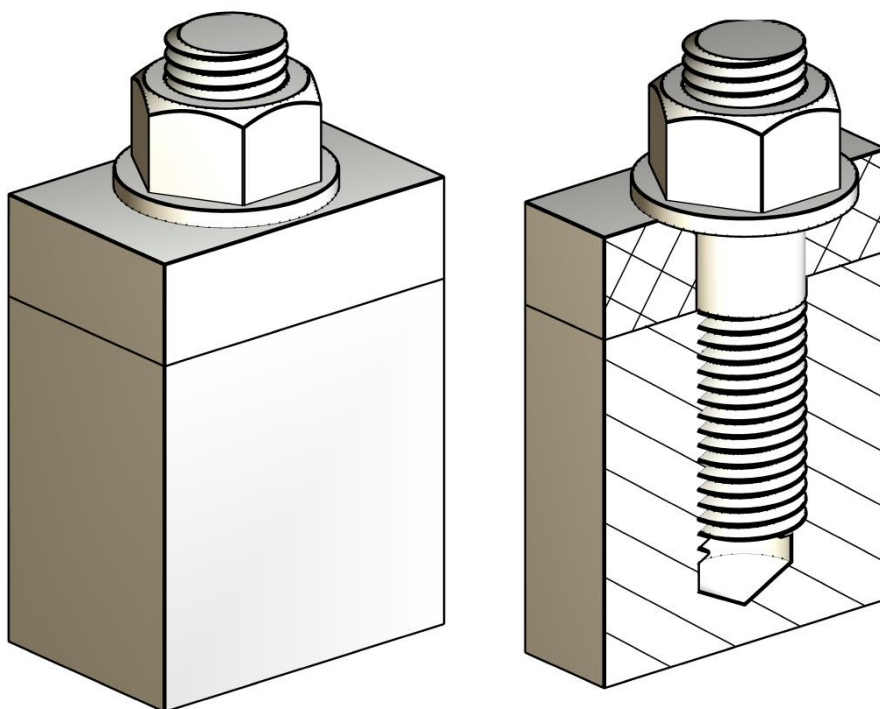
Соединение деталей стандартными крепежными изделиями – шпилькой (ГОСТ 22038-76), шестигранной гайкой (ГОСТ 5915-70, исполнение 2) и круглой шайбой (ГОСТ 11371-78), предотвращающей повреждение гайкой верхней прикрепляемой неметаллической детали (справа изображение выполнено условно в разрезе)
